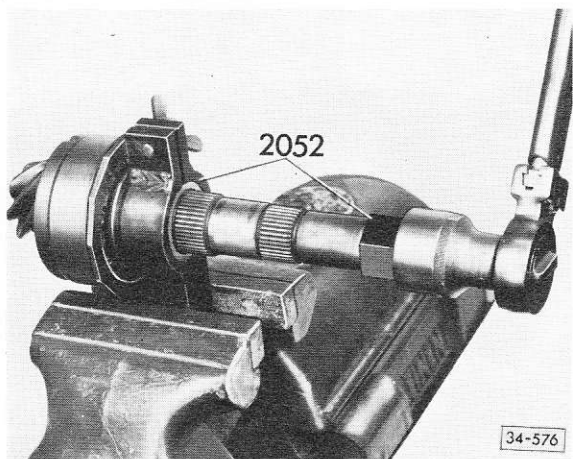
Bague int./roulement à aiguilles: desserrage et serrage
